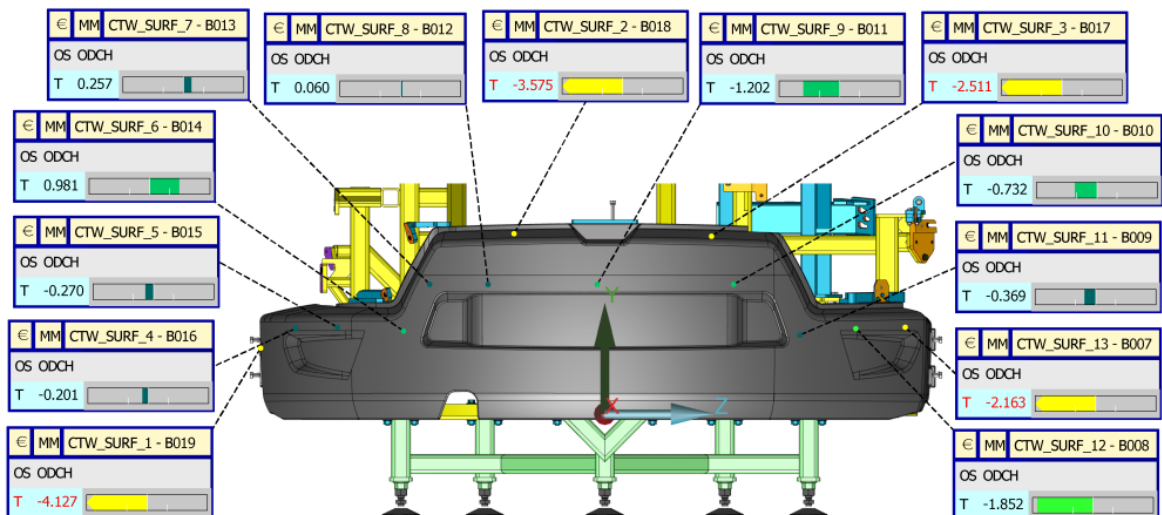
Rozměrová kontrola přípravku 3/6
